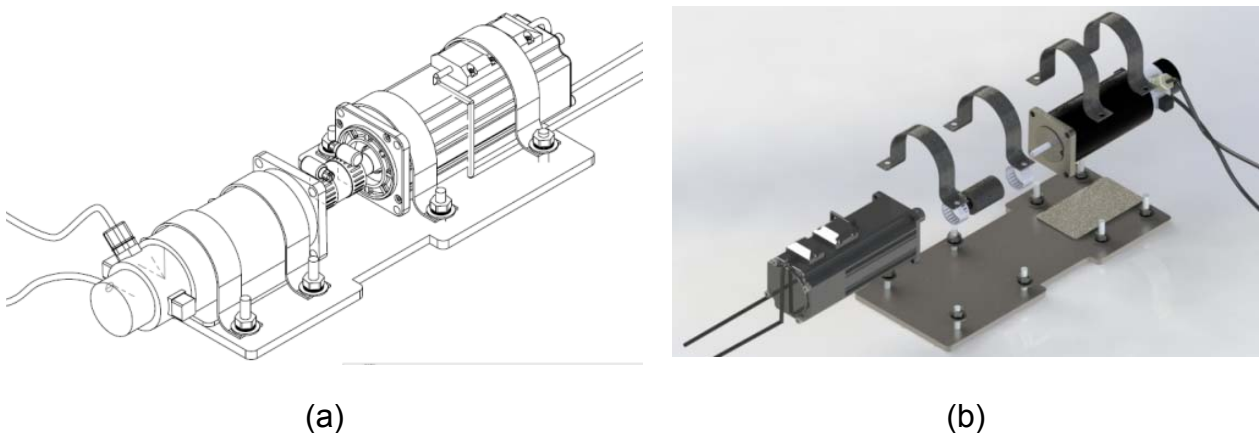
(a) Vista frontal de la plataforma experimental. (b) Explosivo con los componentes de la plataforma experimental.
